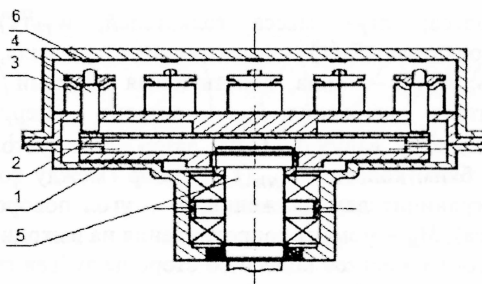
Торцевая волновая зубчатая передача с электромагнитным генератором: 1 – жесткое колесо; 2 – гибкое колесо-пластина; 3 – катушка электромагнита; 4 – толкатель электромагнита; 5 – выходной вал; 6 – ограничитель движения толкателя
